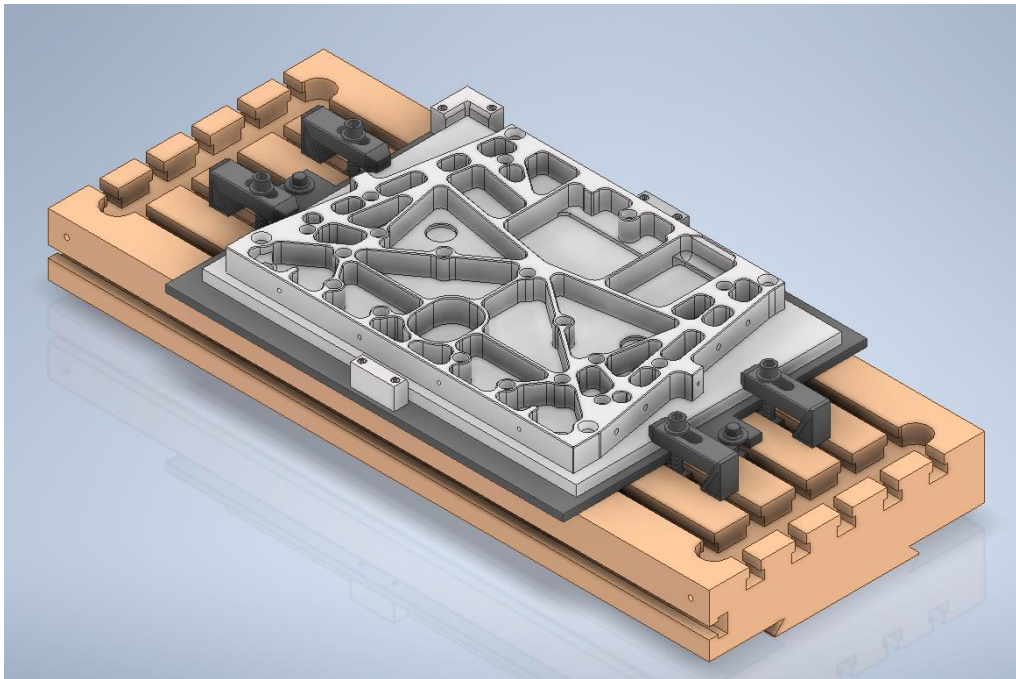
Eine „Fertigungsbaugruppe“ (hier gezeigt in Autodesk Inventor) umfasst neben dem eigentlichen Bauteil (grau) auch den Maschinentisch (orange) und Spannmittel (schwarz). So können CNC-Werkzeugwege auf Kollisionen zwischen Werkzeug und Spannmitteln/Maschinenteilen überprüft werden. Man vermeidet damit nicht nur kostspielige Reparaturen oder Ausschuss durch Kollisionen, sondern ermöglicht auch die personalarme Fertigung, in der man CNC-Maschinen mit ruhigem Gewissen größtenteils unbeaufsichtigt produzieren lassen kann. Wo und wie werden diese CAD-Daten verwaltet?
